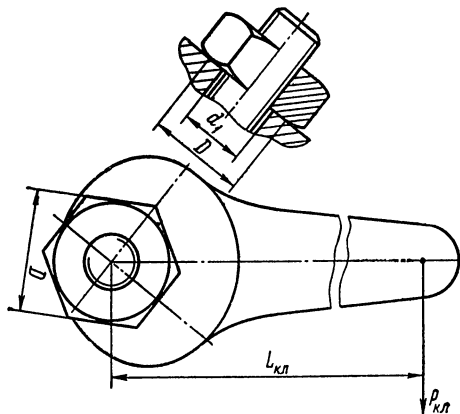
Схема к расчету затяжки резьбового соединения
